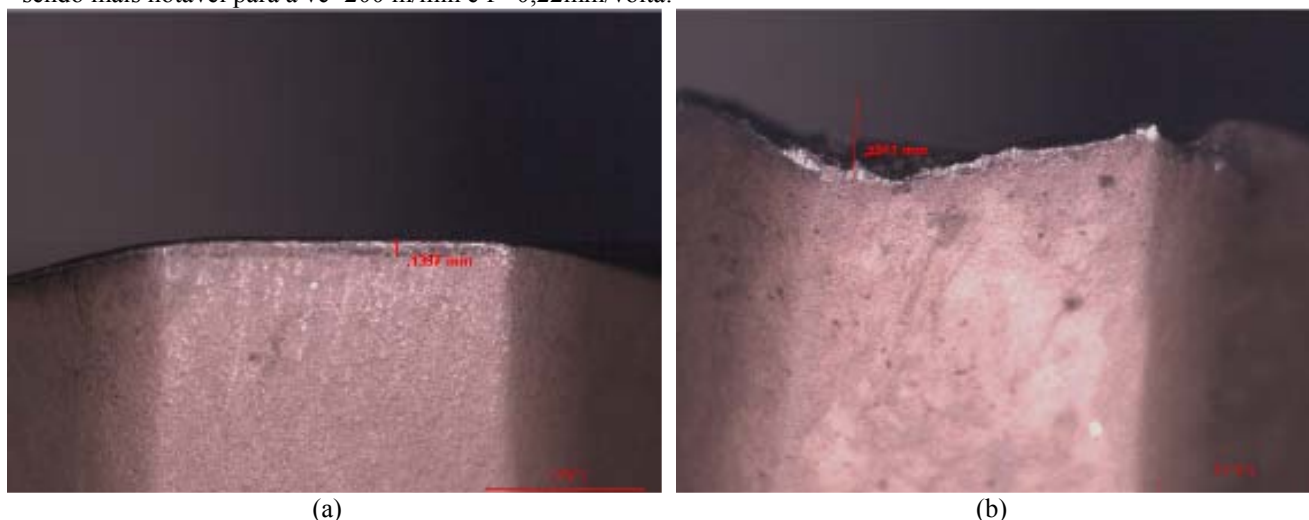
Imagem do desgaste das ferramentas de metal duro após usinagem a seco do aço NB 1047 com  $V_c=260$  m/min e  $f_z=0,22$  mm/volta para a entrada a 90° ; a) 1° passe; b) 6° passe (detalhe para região com lascamento)
